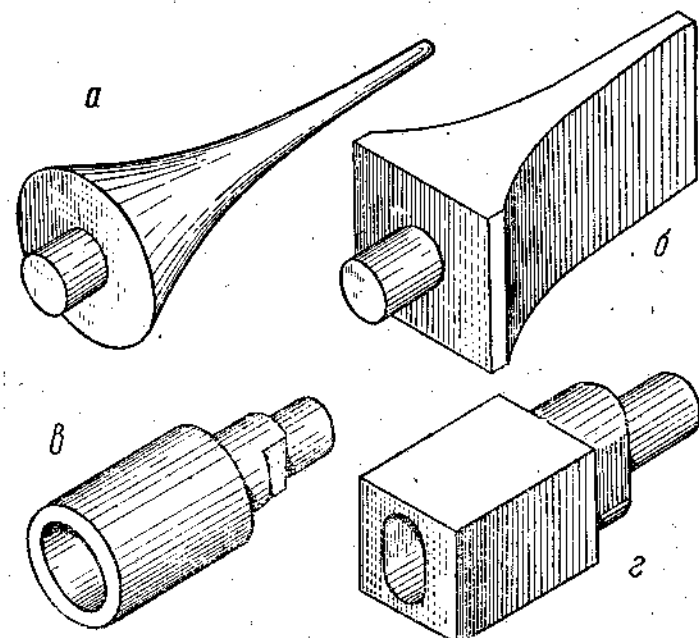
Сменные наконечники для сварки пластмасс ультразвуком: а — точечной сварки, б — ножевой для шовно-шаговой сварки, в — для контурной сварки кольцевых швов, г — для контурной сварки швов прямоугольного сечения.
